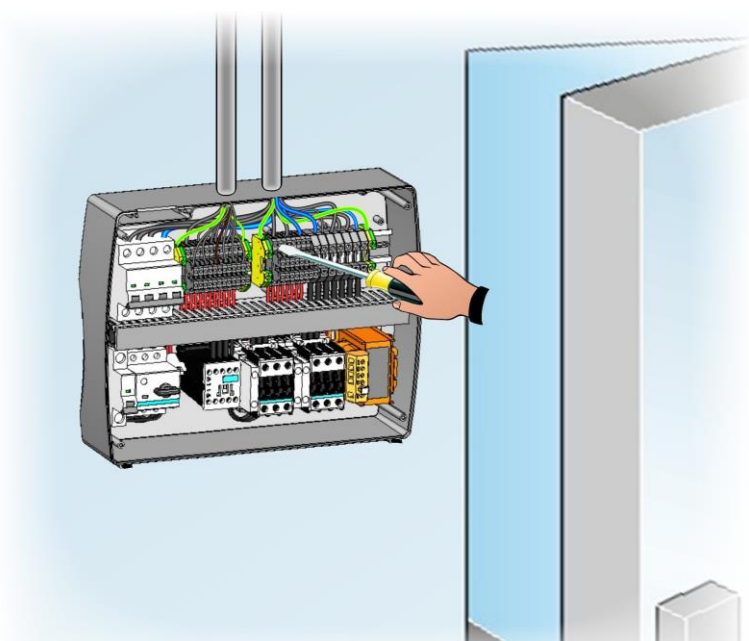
Realizzare ora i collegamenti elettrici come indicato nel capitolo seguente.
